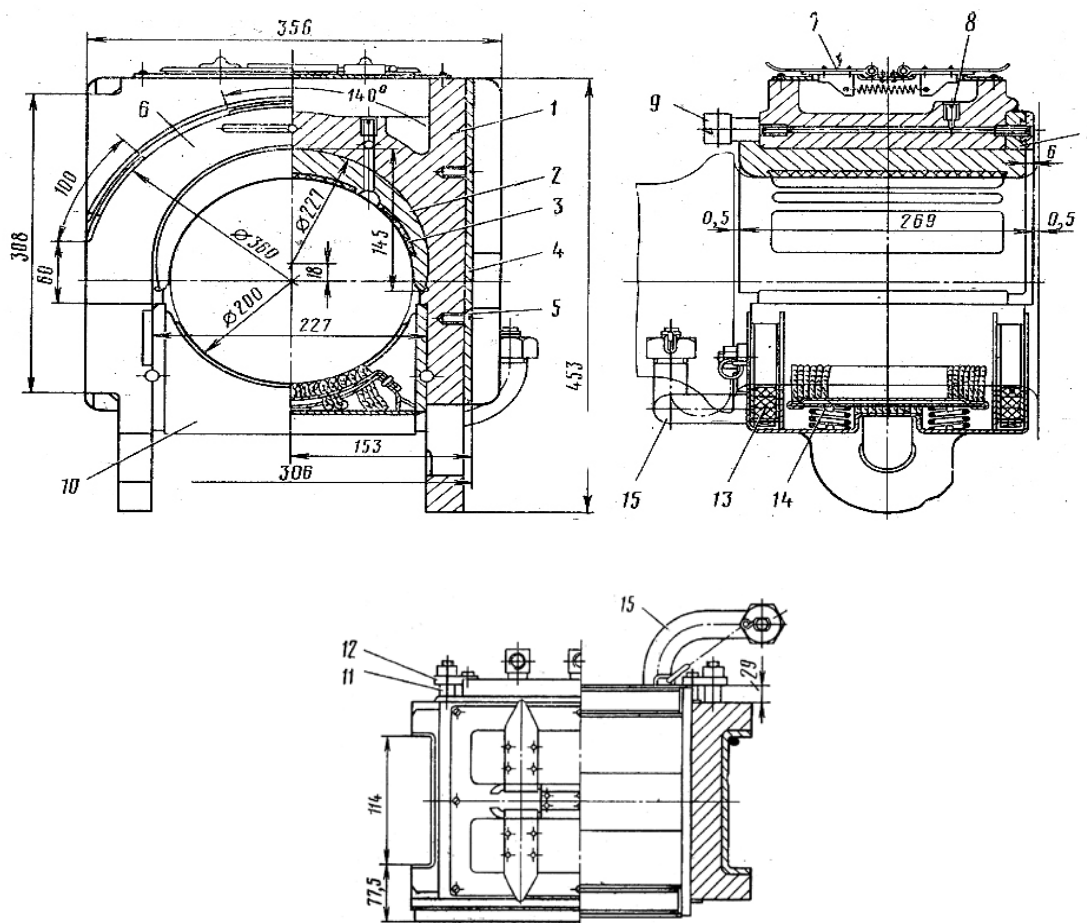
Унифицированная букса сцепных осей паровозов ЭР: 1 – корпус буксы; 2 – подшипник; 3 – колодцы для баббитовой заливки; 4 – наличник; 5 – винт; 6 – торцовая шайба; 7 – крышка; 8 – винт-заглушка; 9 – штуцер; 10 – подбуксовая коробка; 11 – стержень; 12 – планка; 13 – манжета; 14 – польстер; 15 – трубка
